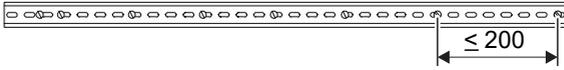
Fixation du rail de montage (spécifications en mm)
